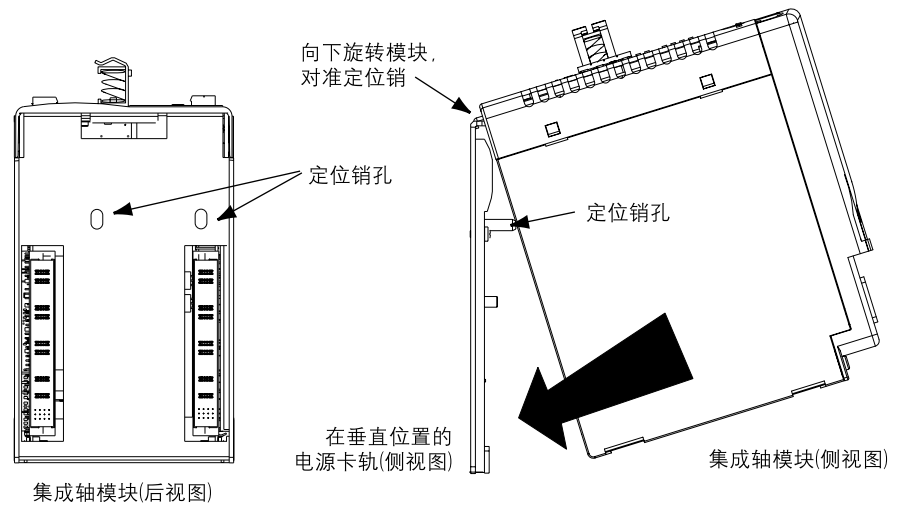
在电源卡轨上安装 Kinetix 6000 部件
